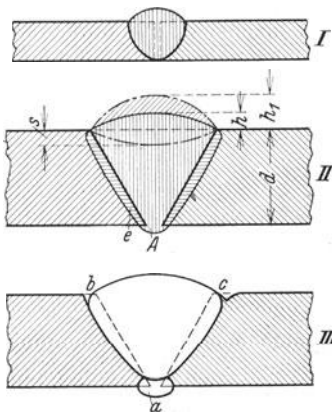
Querschnitte von I- und V-Schweißen.
